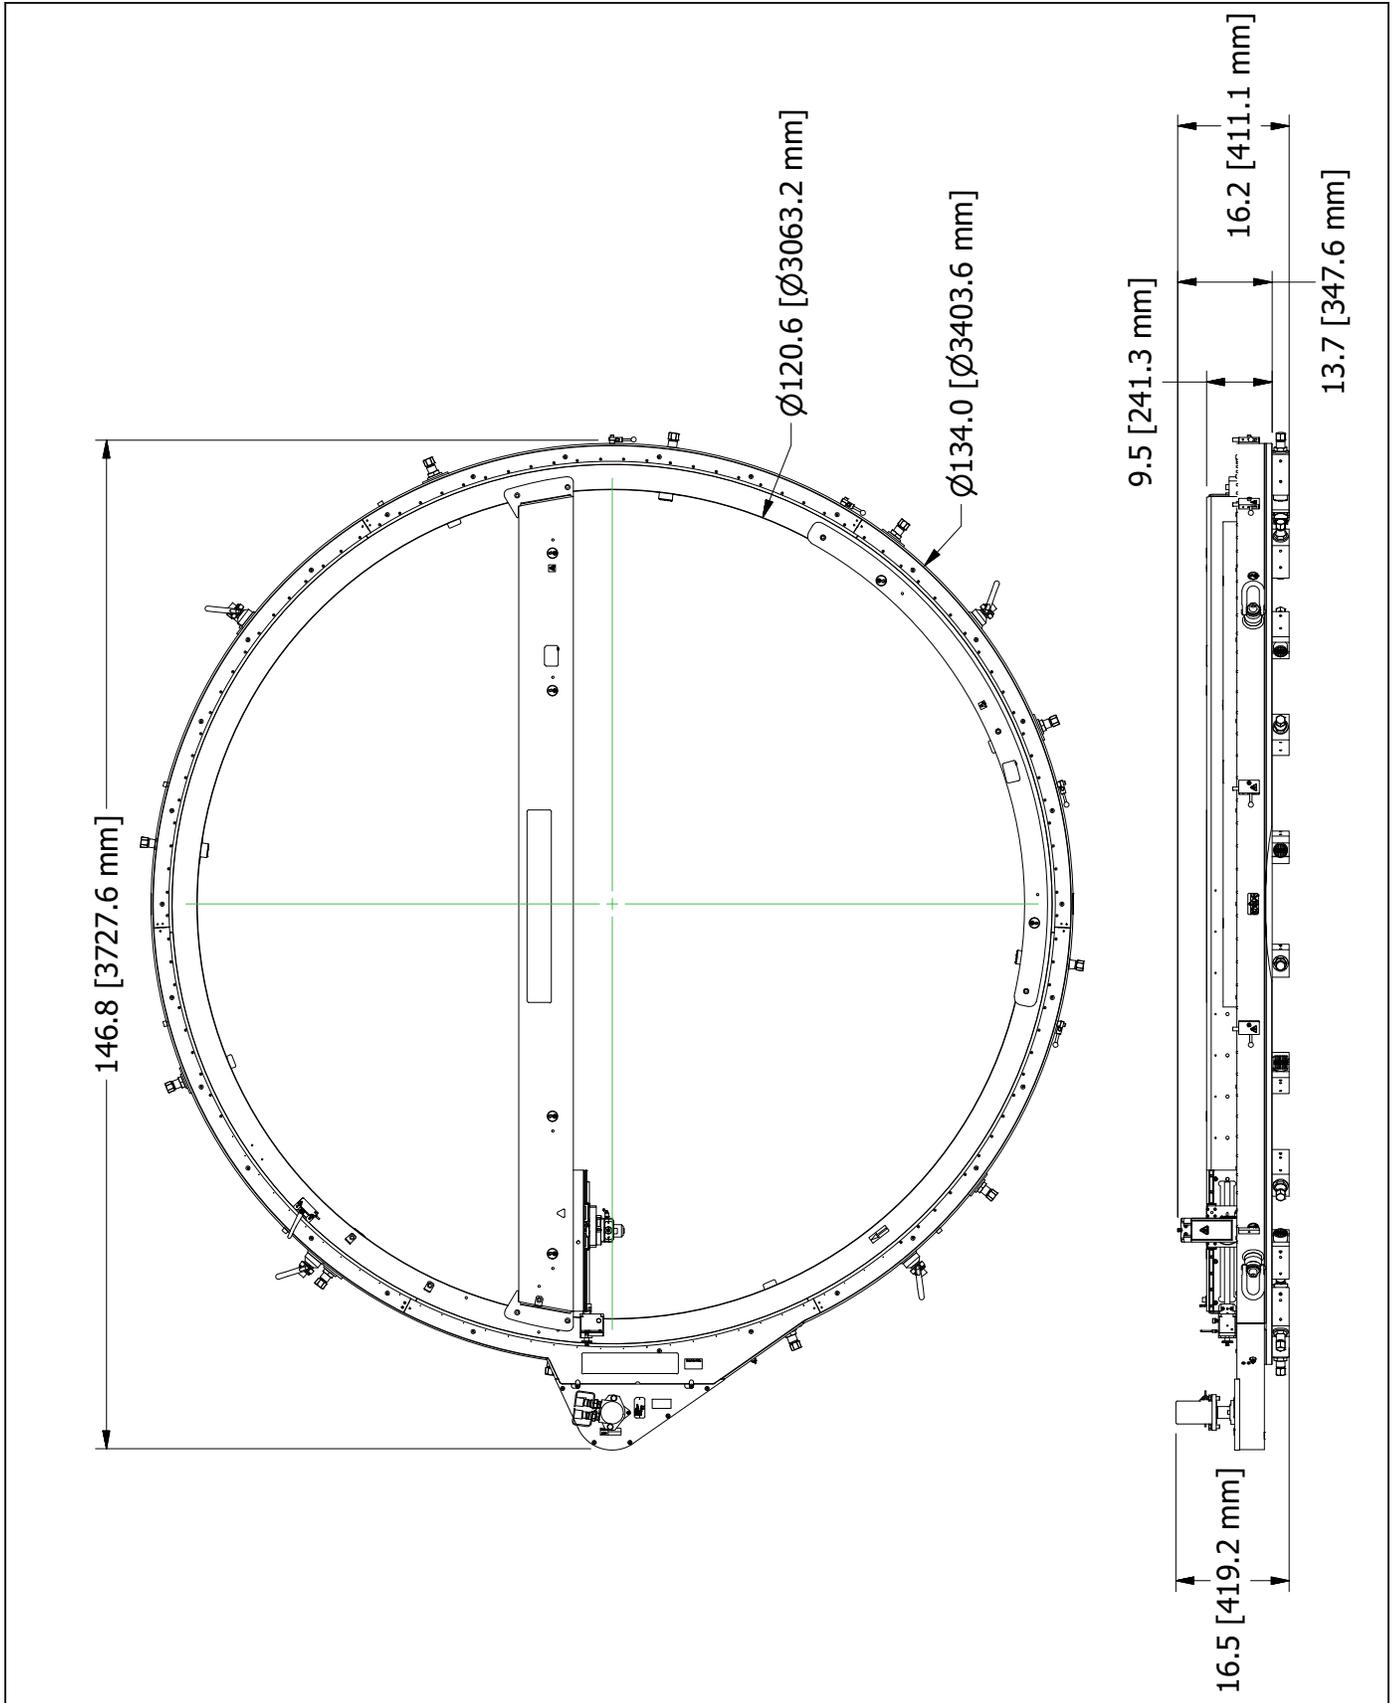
DIMENSIONS DE LA SURFACEUSE RAPIDE ODF120 SPEED FACER (REF. 7639-S1)
